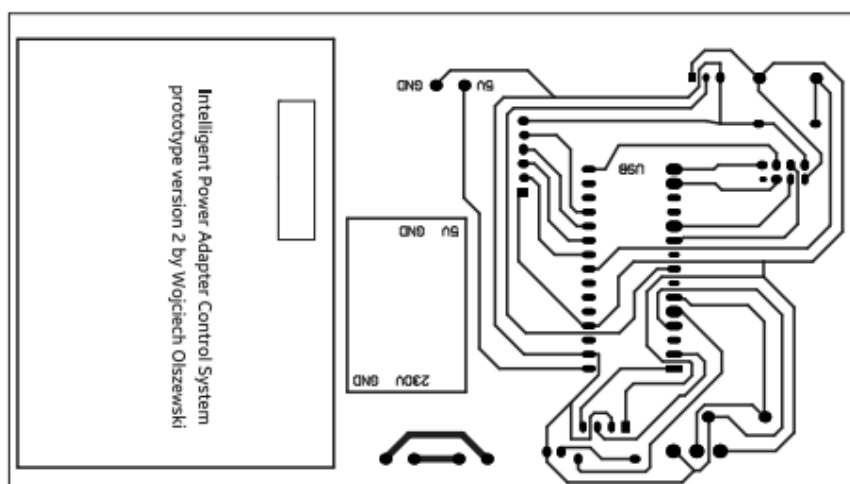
Pierwszy prototyp PCB układu listwy
